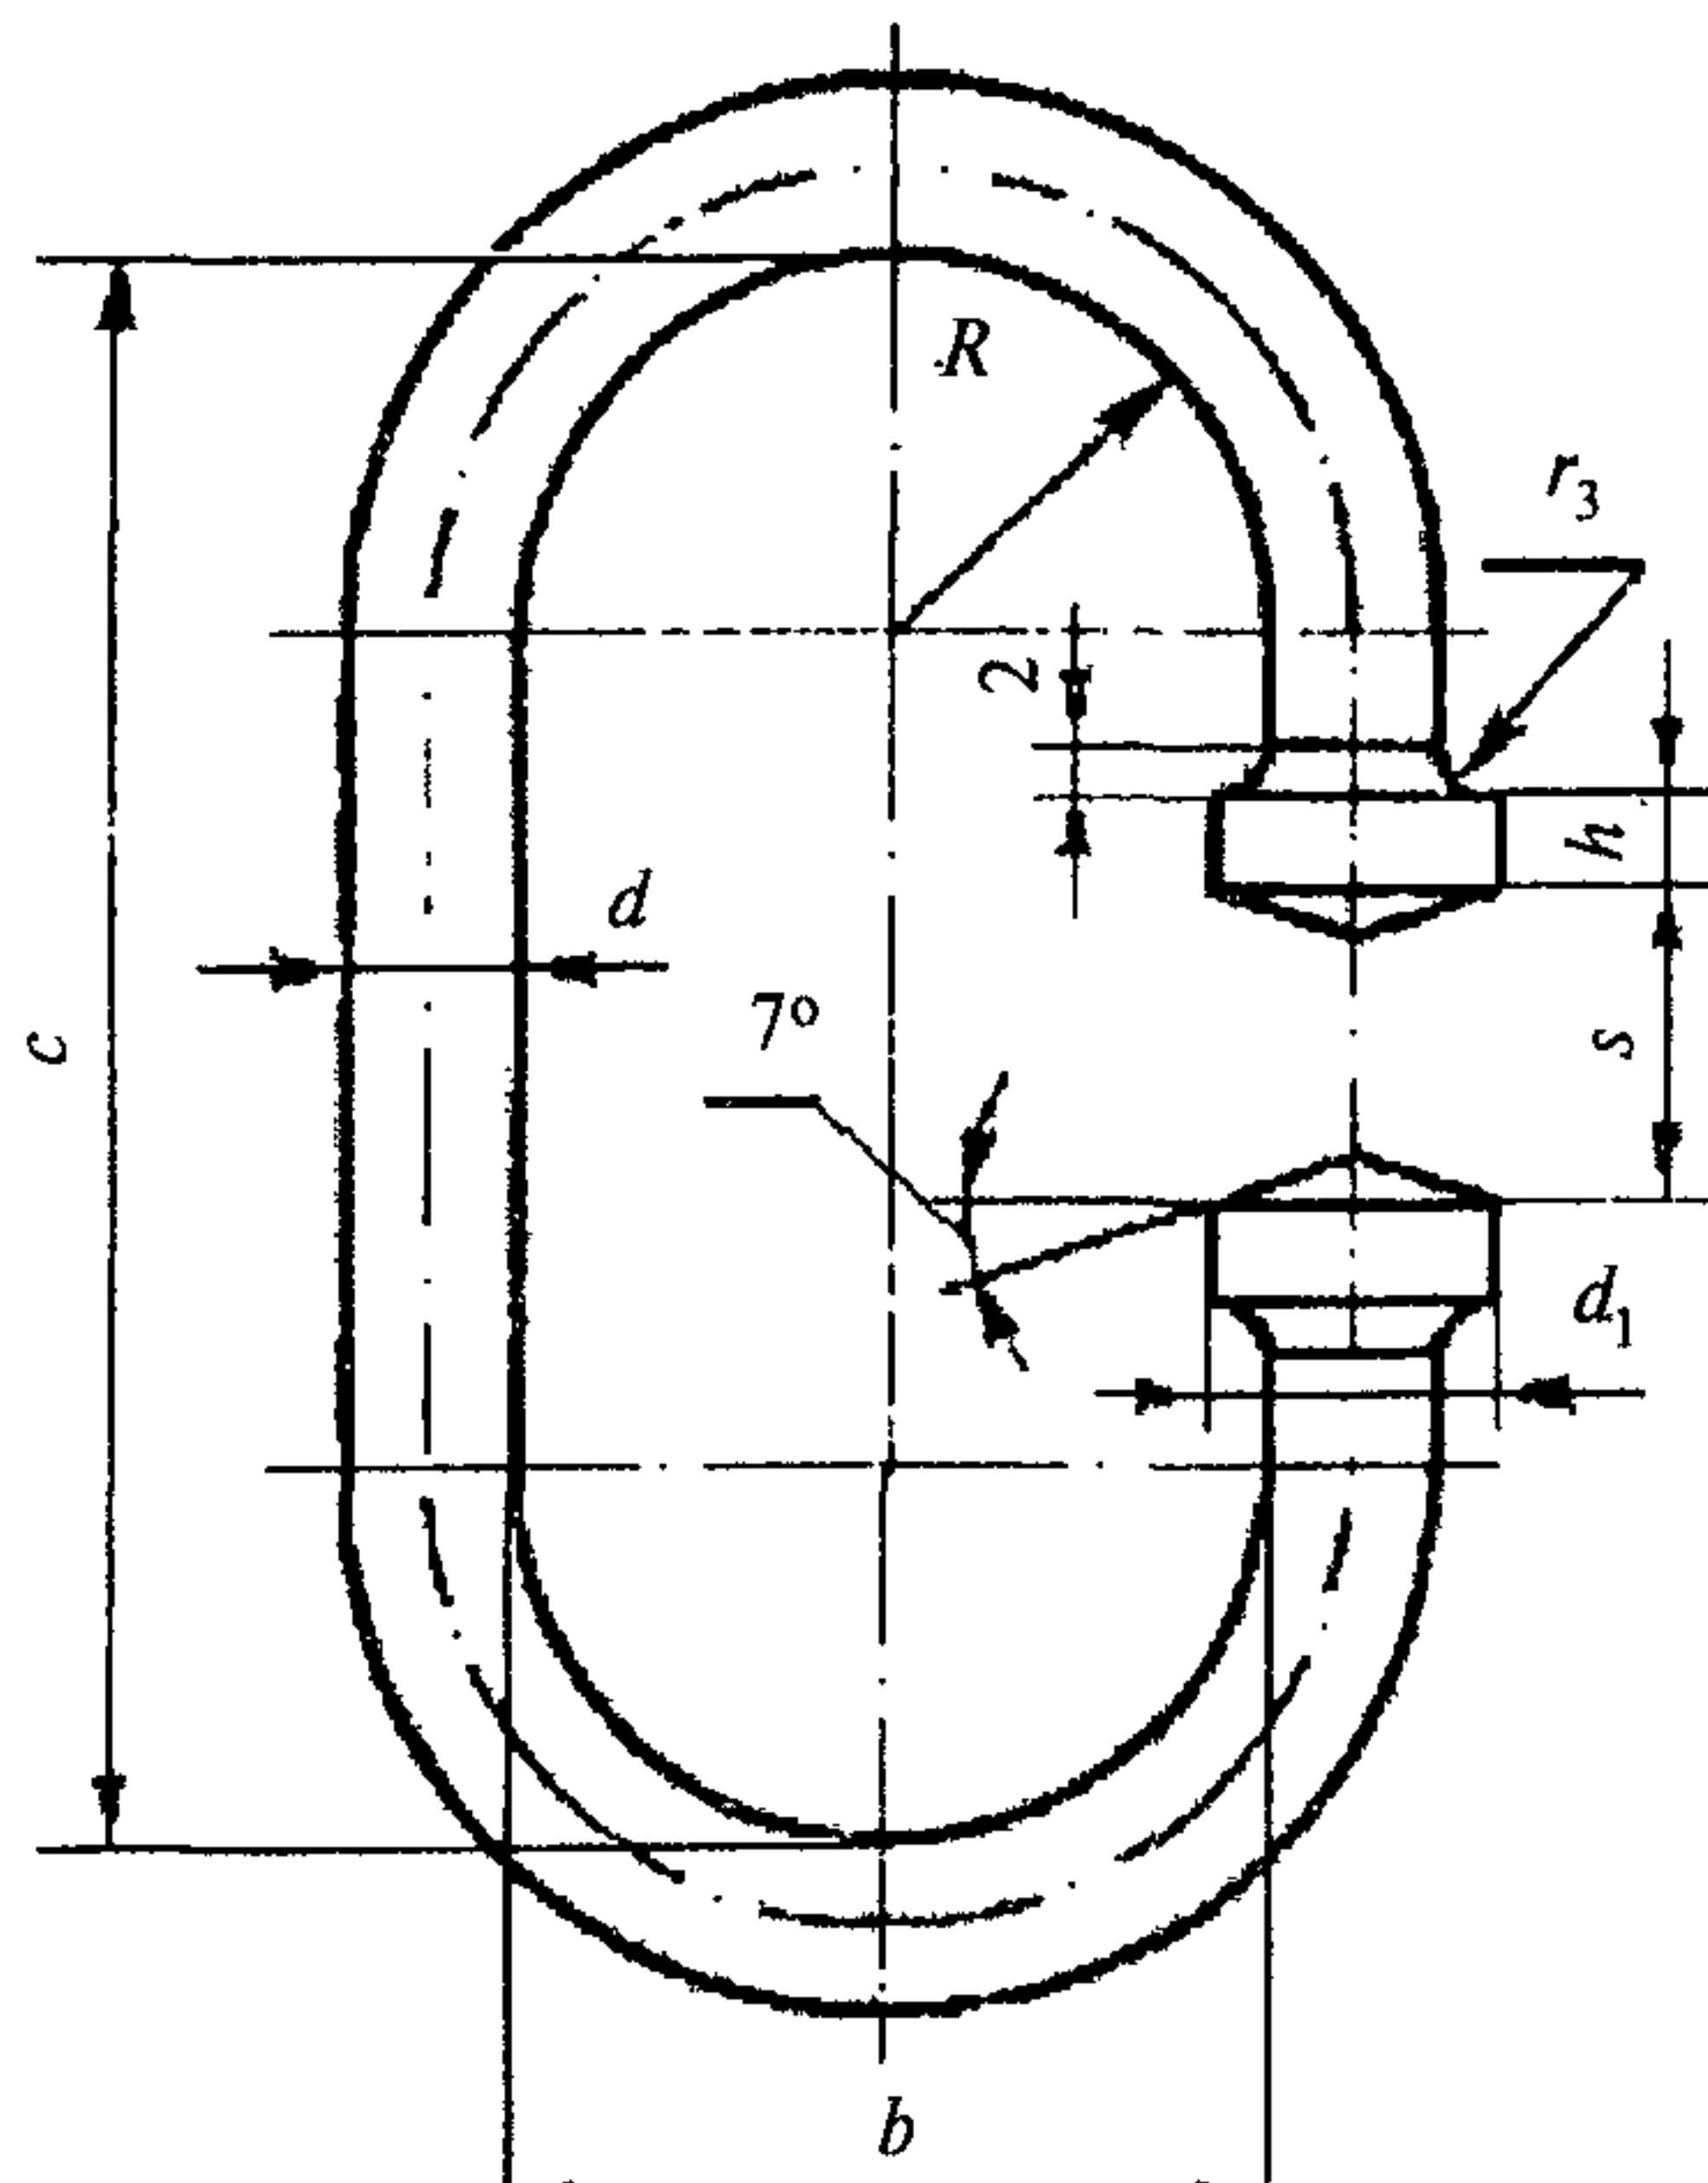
Скоба Сов для звеньев Ров с допускаемой нагрузкой до 2 тс
